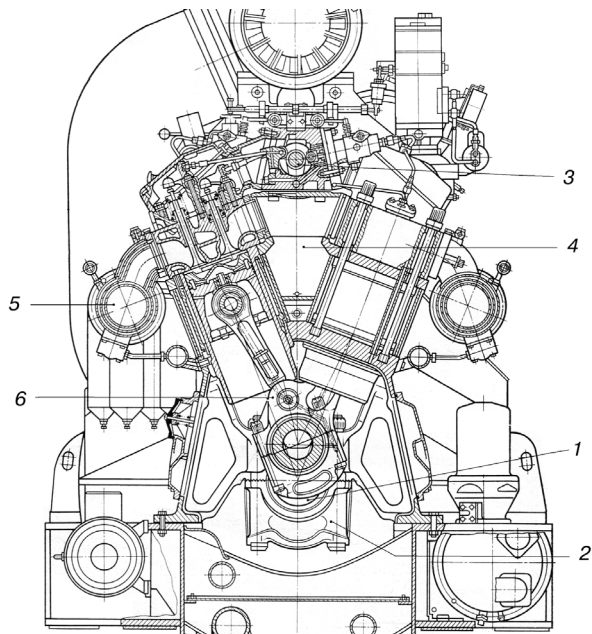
Дизель 1-5Д49, поперечное сечение:
